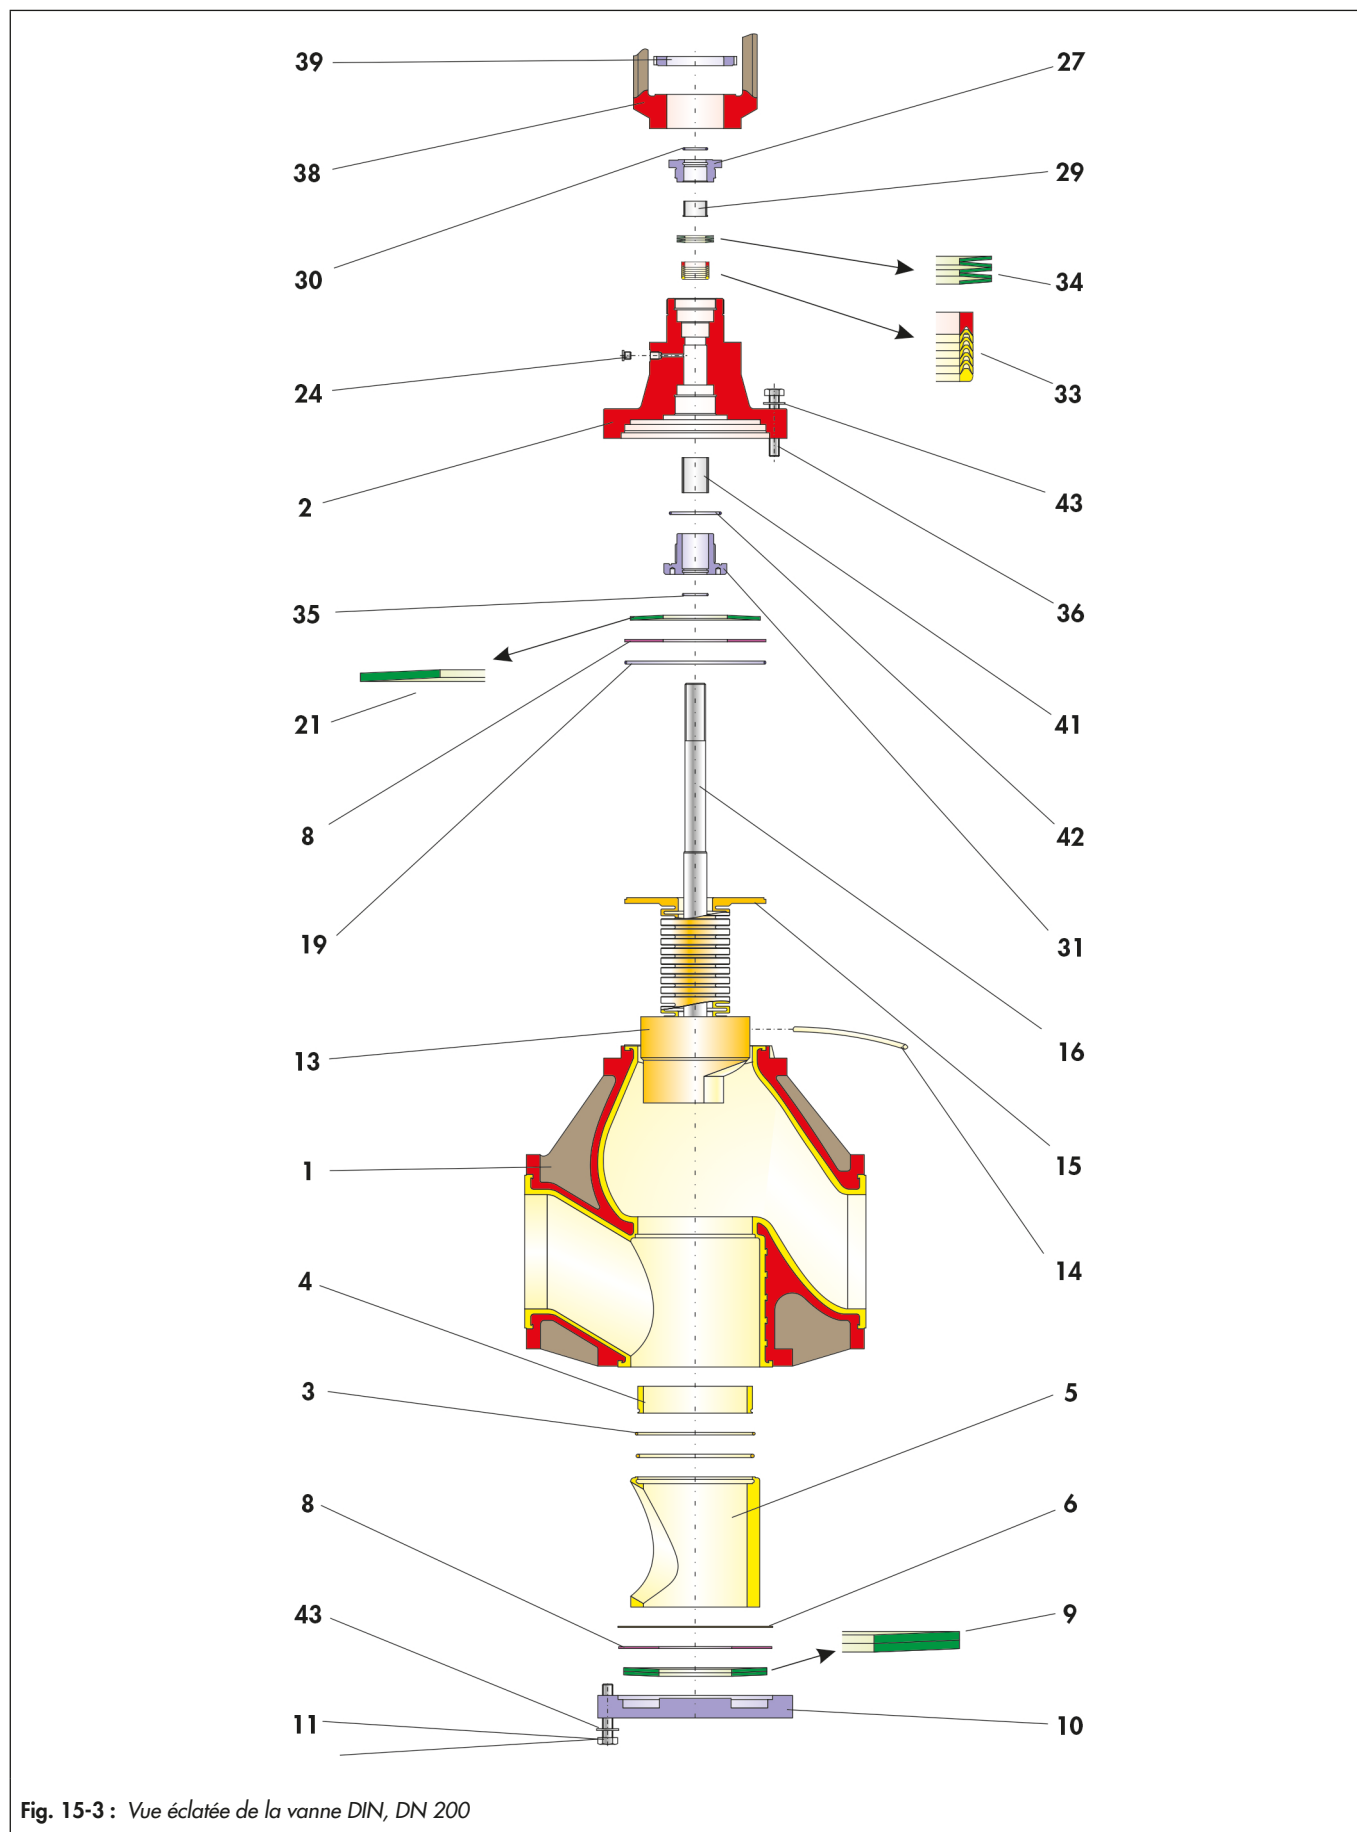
Vue éclatée de la vanne DIN, DN 200
